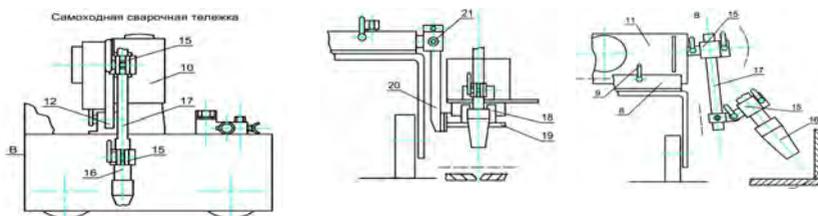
Общая конструкция самоходной сварочной тележки для автоматизированного мобильного технологического комплекса сварки
